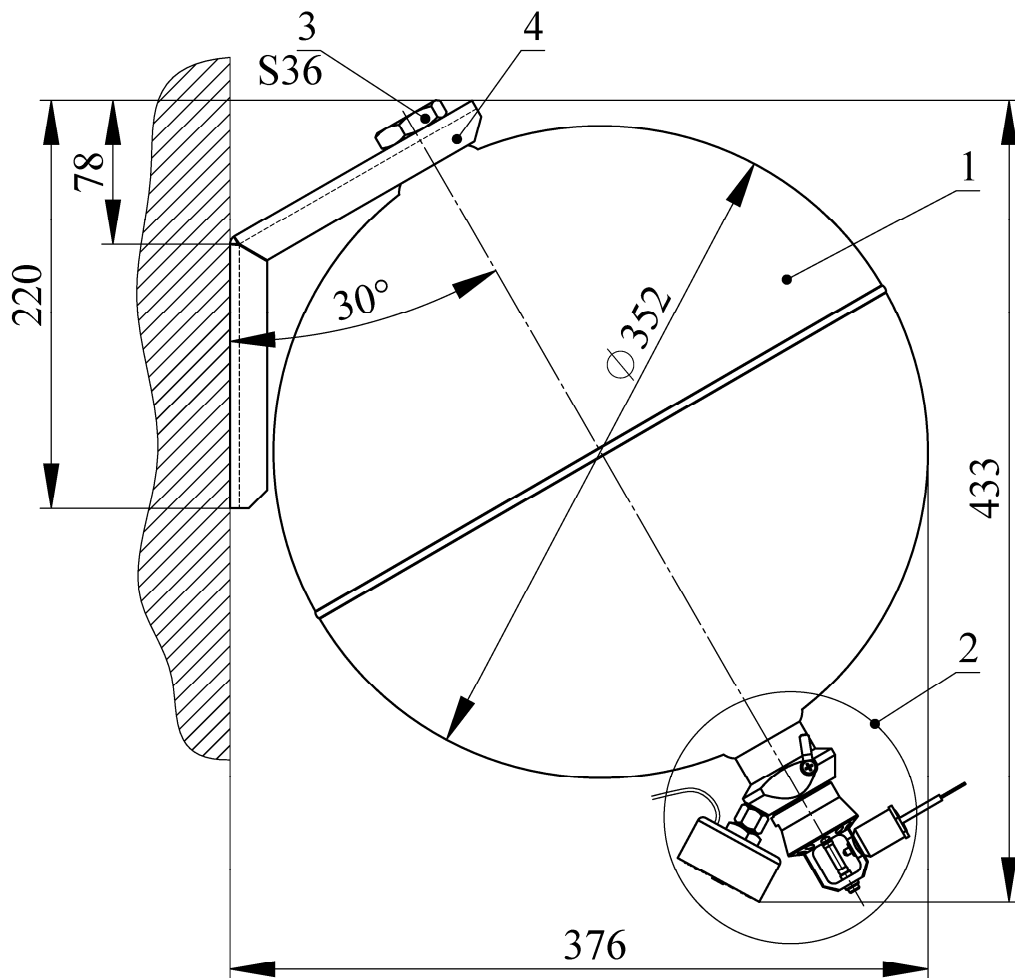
Общий вид и присоединительные размеры креплений
